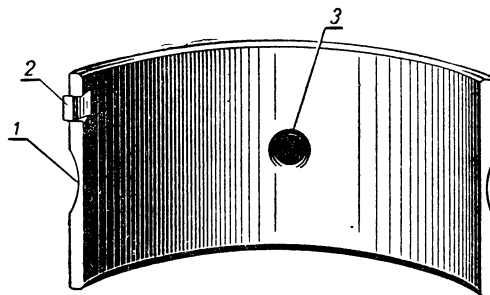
Верхний вкладыш шатунного подшипника дизелей Д-54А и Д-75:
